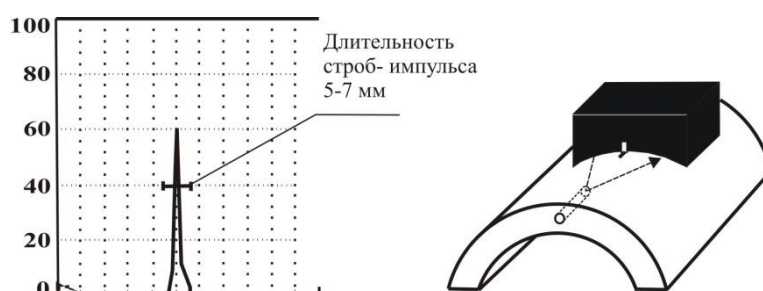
Схема типовой настройки строб-импульса при контроле стыковых сварных соединений труб с применением РС ПЭП «хордового» типа
